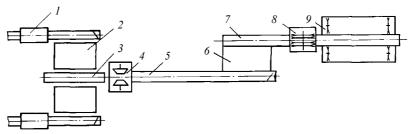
Схема фрезерно-брусующей линии: I – окорочные станки; 2 – накопители; 3 – подающий конвейер; 4 – фрезерно-брусующий станок; 5, 6, 7 – конвейеры; 8 – многопильный круглопильный станок; 9 – торцовочные станки
